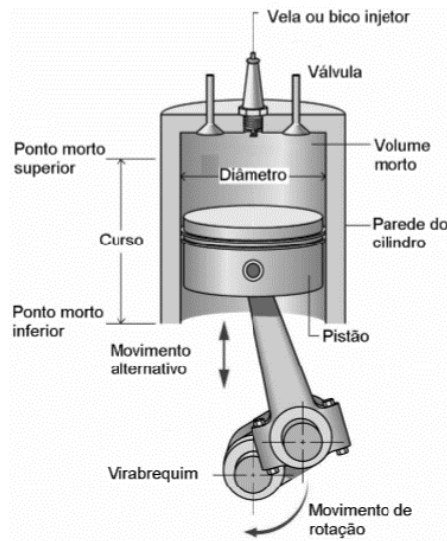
Conjunto pistão - cilindro de um motor de combustão interna.
